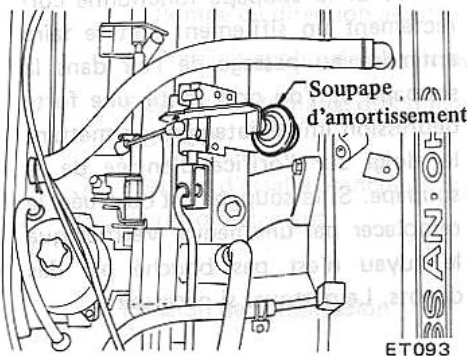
Réglage de la soupape d'amortissement (double carburateur)
